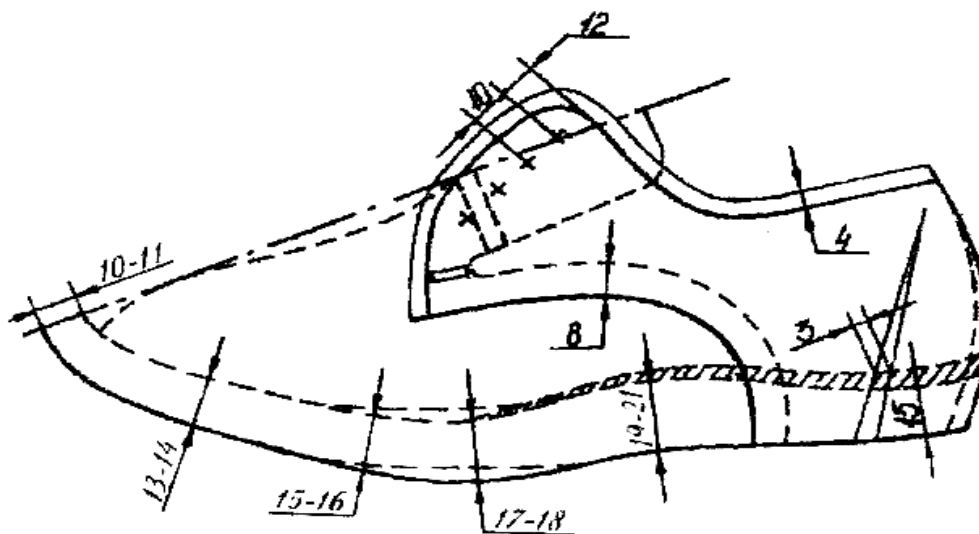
Корегування ґрунд-моделі і побудова креслення деталей напівчеревика з настроченими берцями
